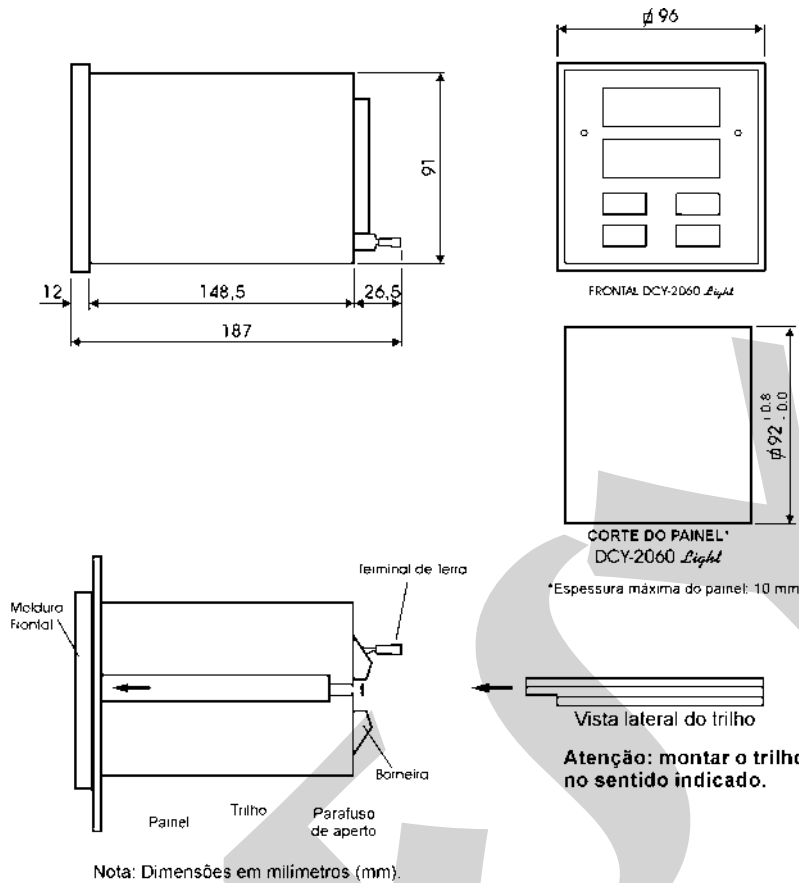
Desenho dimensional, corte e vista lateral da montagem no painel do controlador DCY-2060 *Light
